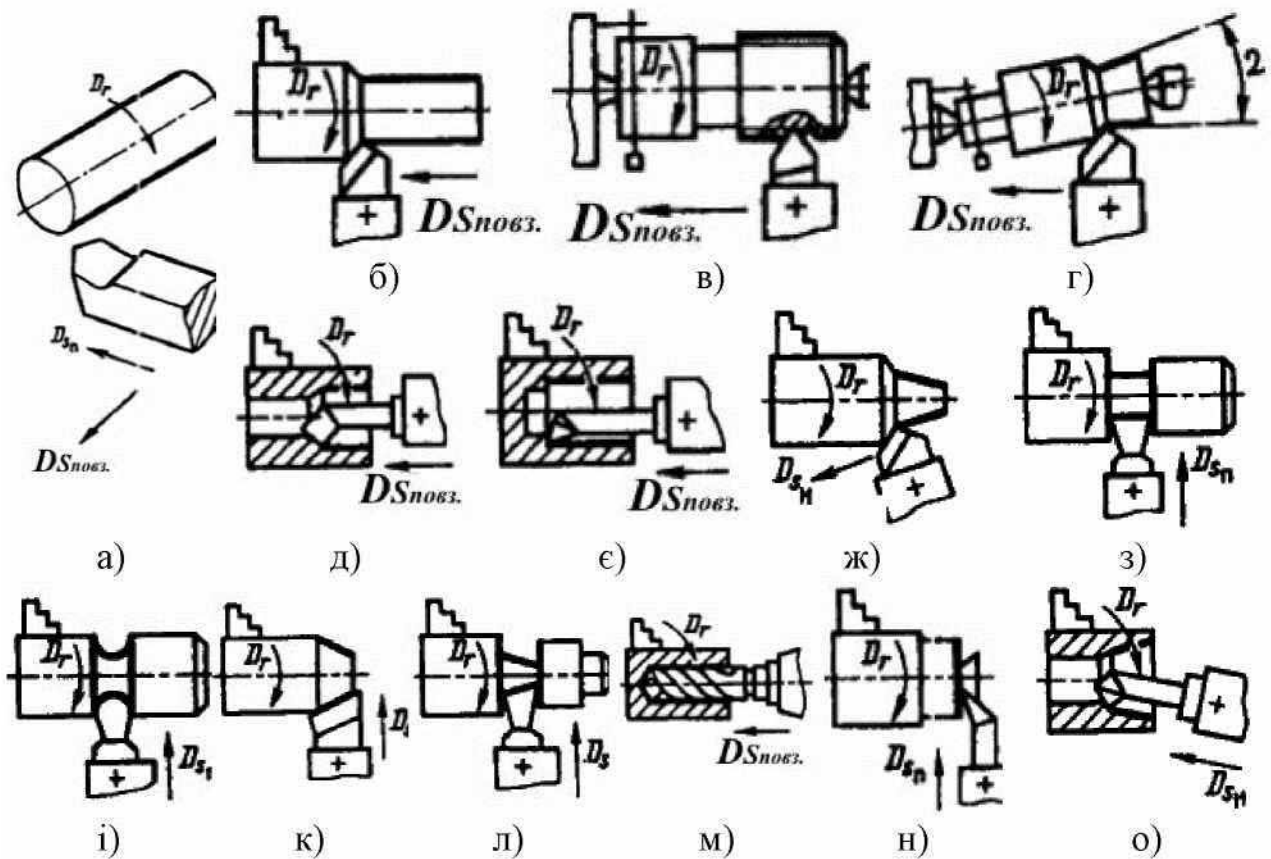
Типові схеми обробки поверхонь заготовок на верстатах токарної групи
